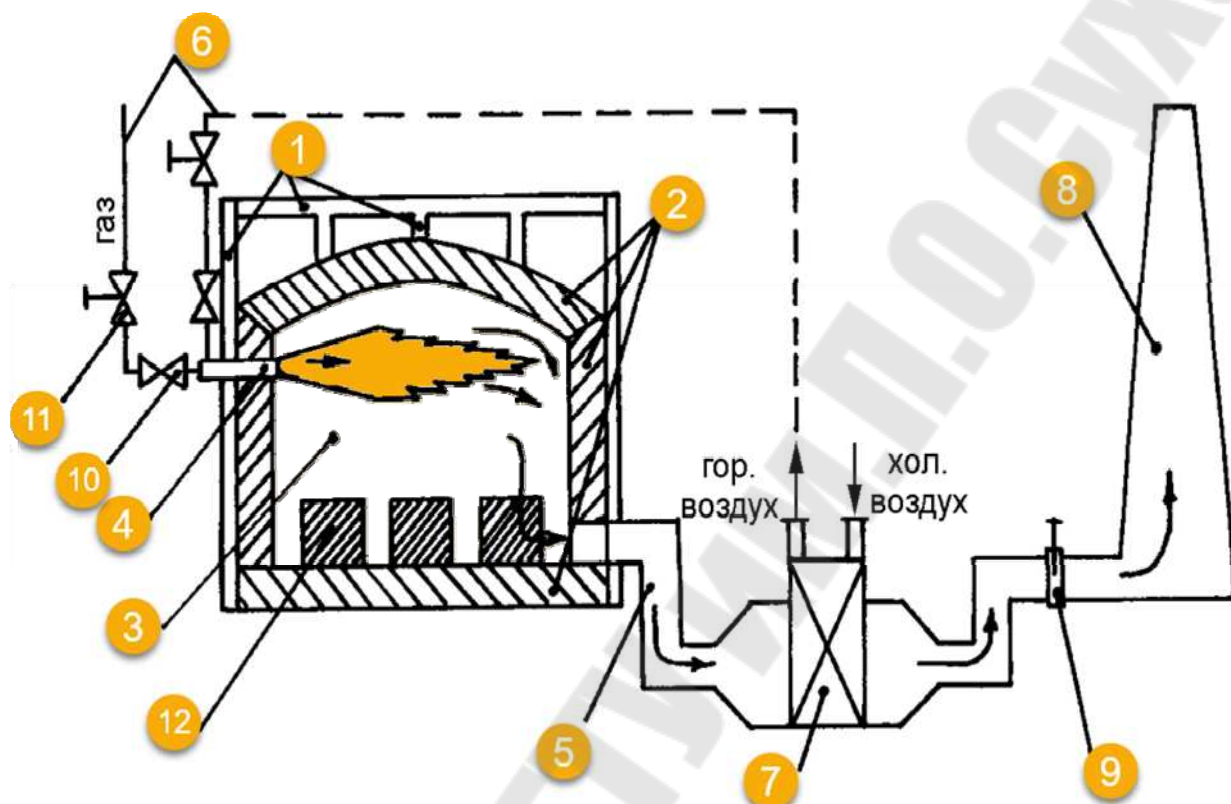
Основные элементы печи: 1 - металлический каркас; 2 - футеровка (свод, стены, подина); 3 - рабочее пространство печи; 4 - горелка; 5 - бора (дымоходы); 6 - газозухопроводы; 7 - теплообменник; 8 - дымовая труба; 9 - дымовой шибер; 10 - дроссели; 11 - задвижки; 12 - нагреваемый материал
